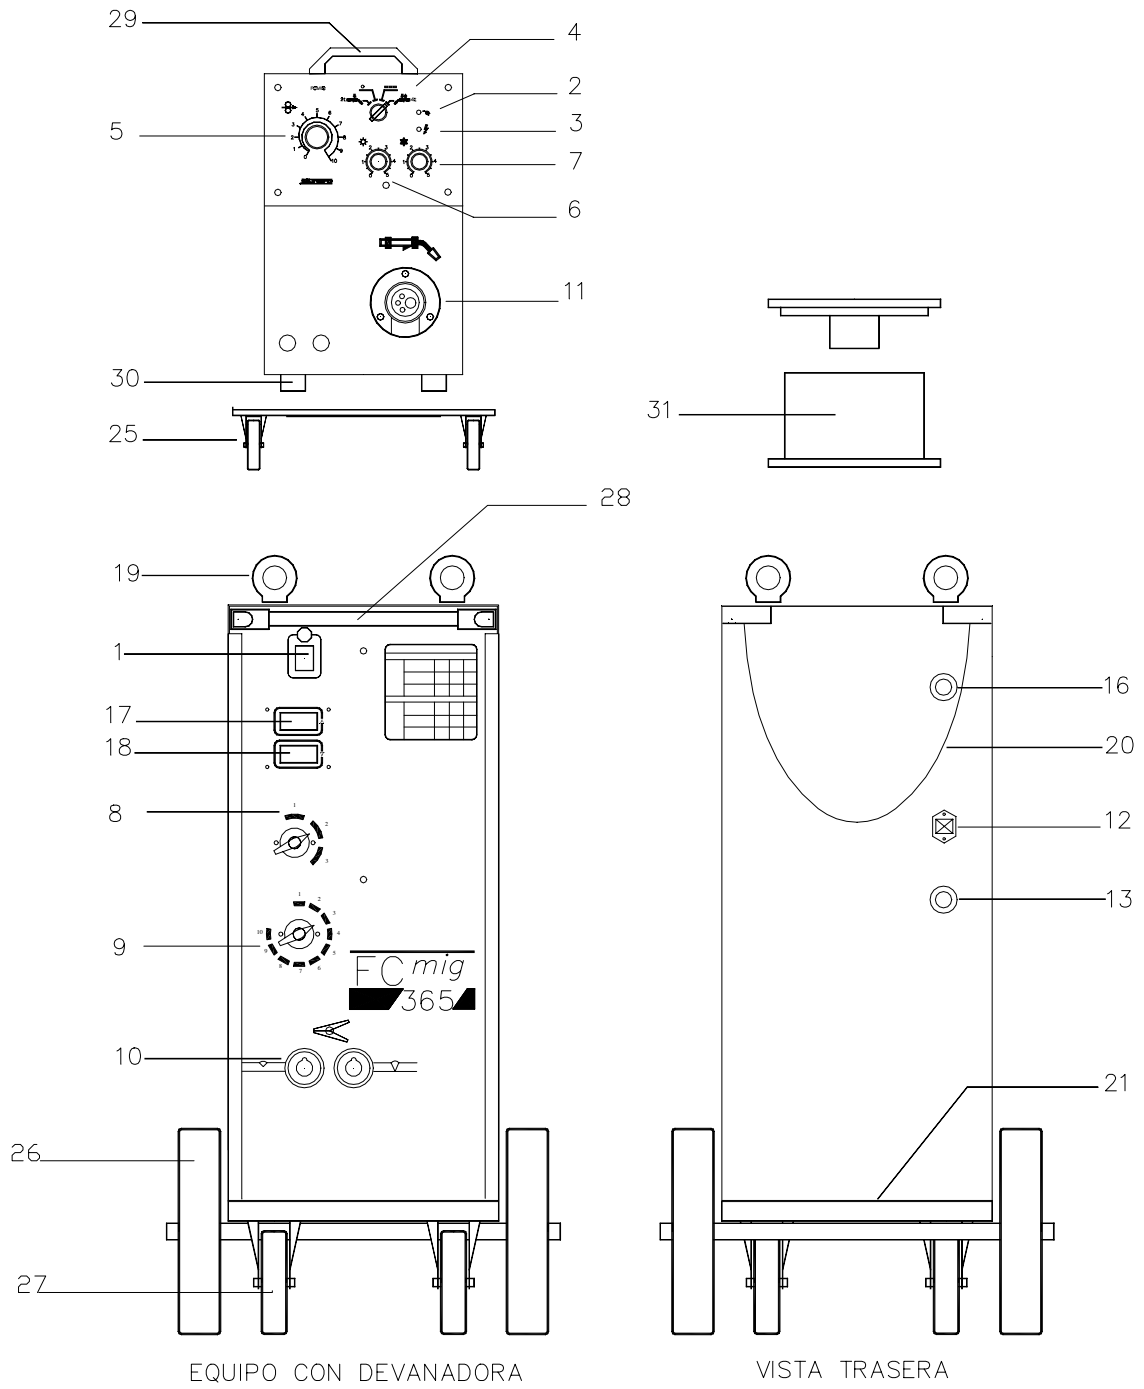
Vista frontal y trasera equipo soldadura
